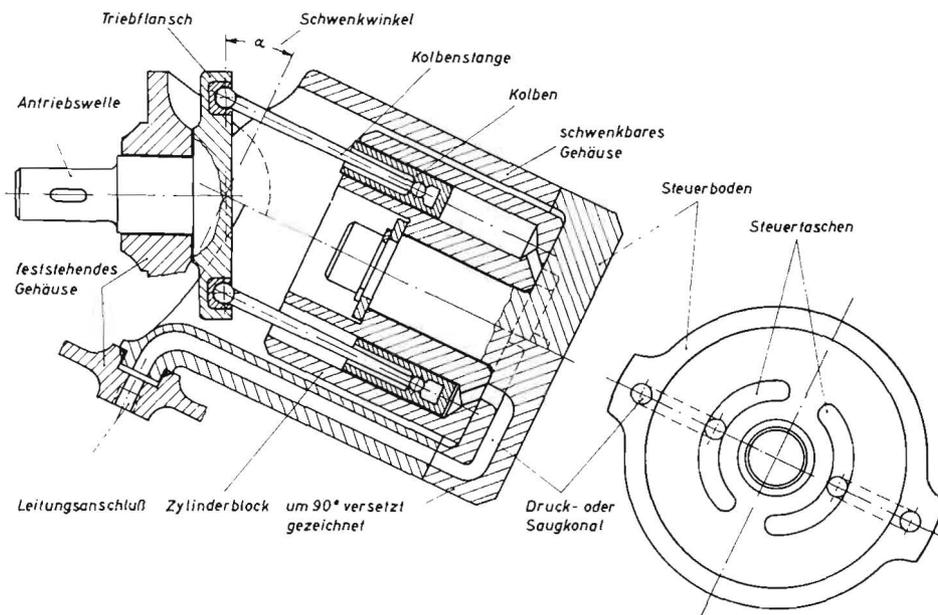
(rechts): Grundaufbau der Axialkolbenmaschine mit schwenkbarem Zylinderblock
